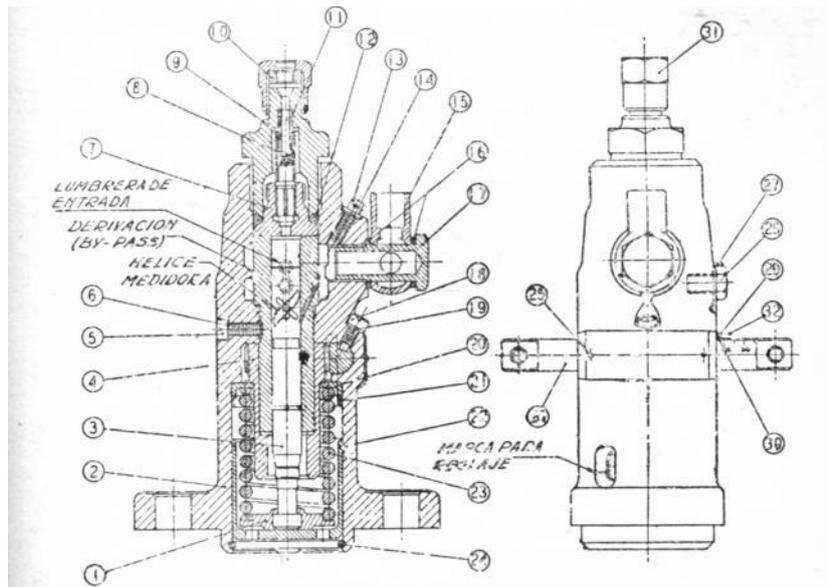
Corte a través de una bomba Bendix-Scintilla
